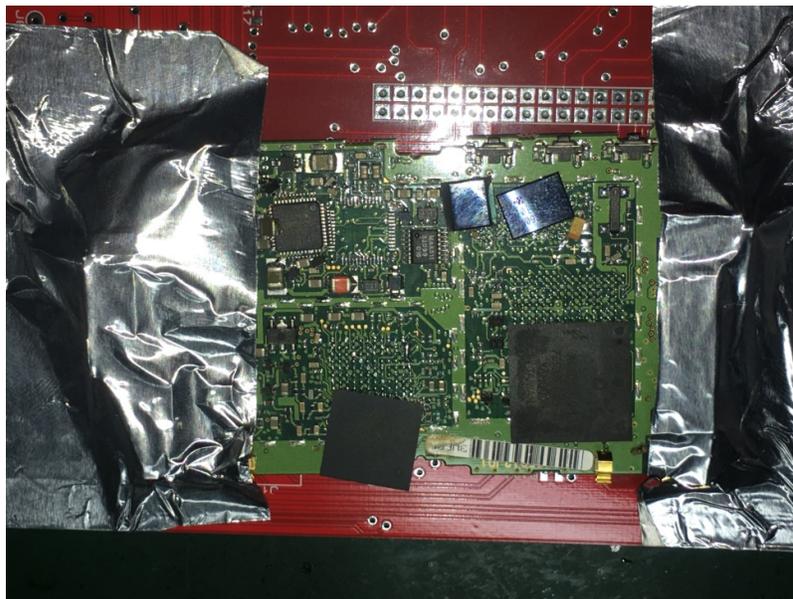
Placa de sacrificio (en verde) con los integrados BGA desoldados. La placa roja, al fondo, se utilizó para disipar el calor del PCB pequeño y generar problemas.
